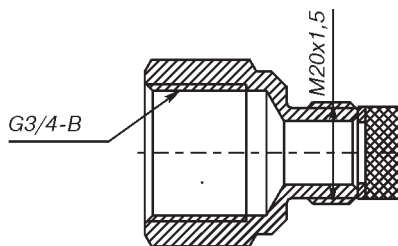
Кабельный ввод с внутренней цилиндрической резьбой G3/4" (G3/4).
